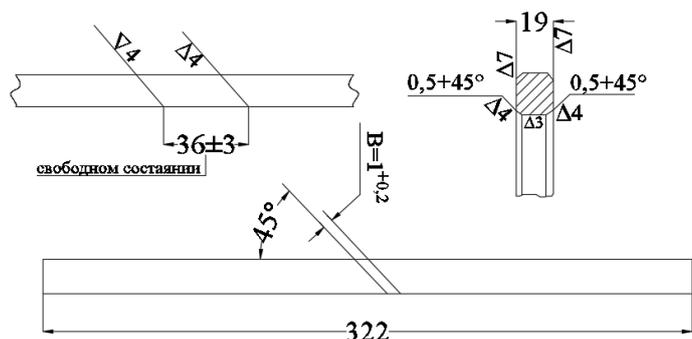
Чертеж детали – кольцо поршневое \varnothing 322 мм
